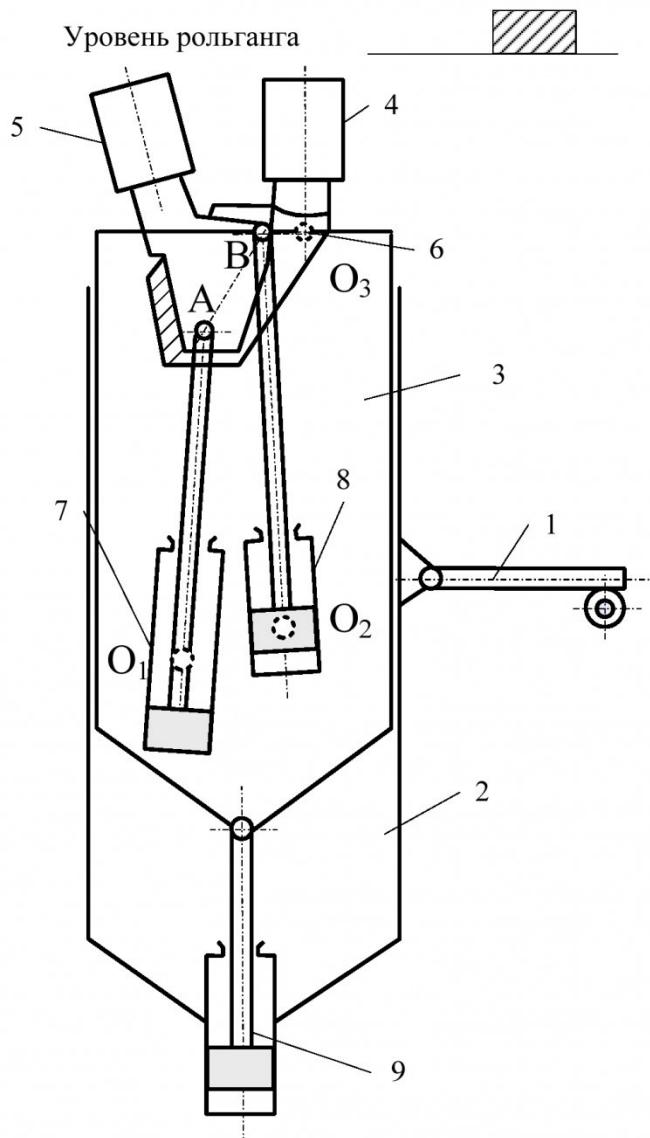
Схема устройства роликового кантователя прокатного стана с гидравлическим приводом:
